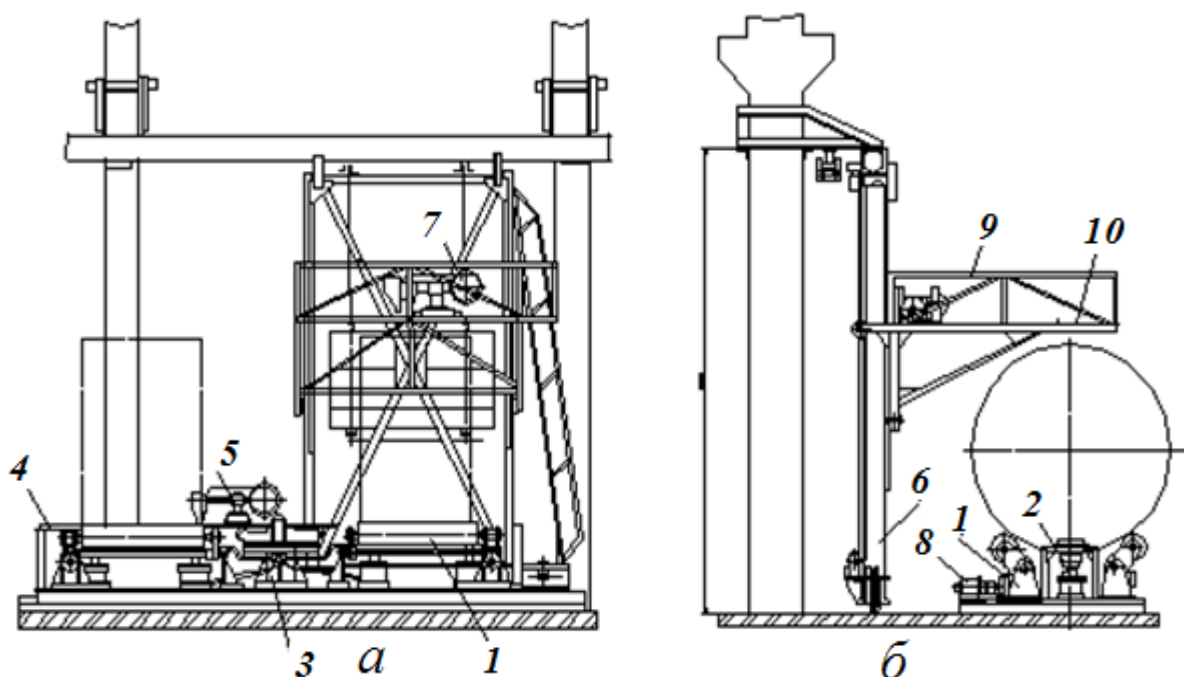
Установка для двох стороннього автоматичного зварювання поздовжніх швів обичайок: а – вид з переді; б – вид з боку; 1 – роликоопори; 2 – флюсові подушки; 3 – підставка; 4 – пересувні напрямні; 5, 7 – зварювальний трактор; 6 – велосипедний візок; 8 – електромотор; 9 – балкон; 10 – напрямні
